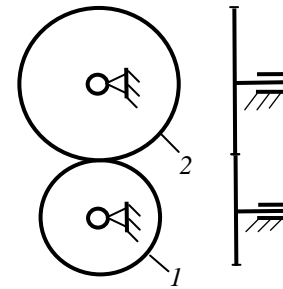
Зубчатая передача с внешним зацеплением колёс
